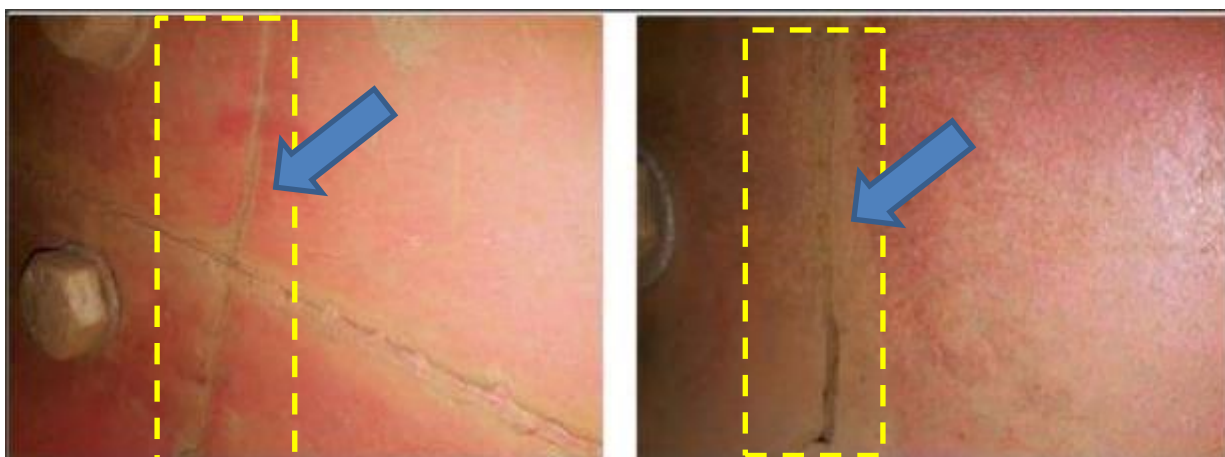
Desenho Esquemático da Região da Trinca na Viga do Filtro Prensa.
